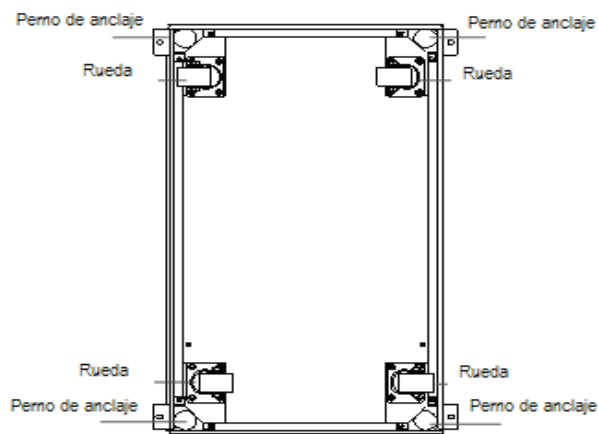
Estructura de soporte y desplazamiento (Vista inferior)
